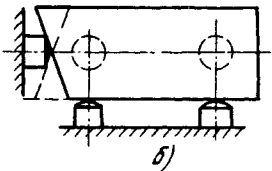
Установка опор в приспособлении, повышающая определенность базирования заготовки по направляющей и опорной базам
